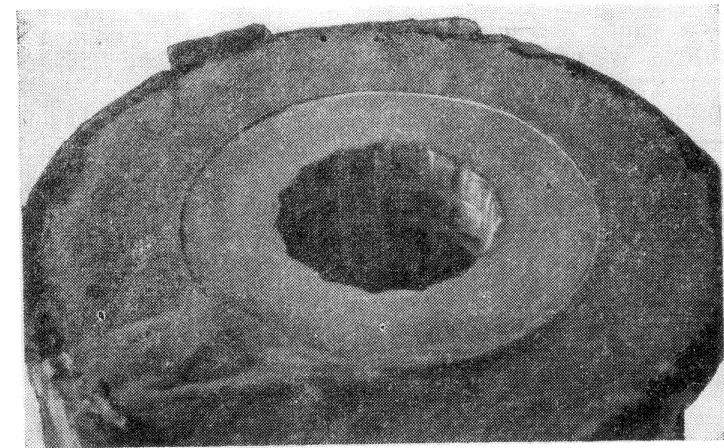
Форма для отливки корпуса реактора с орнаментом.
